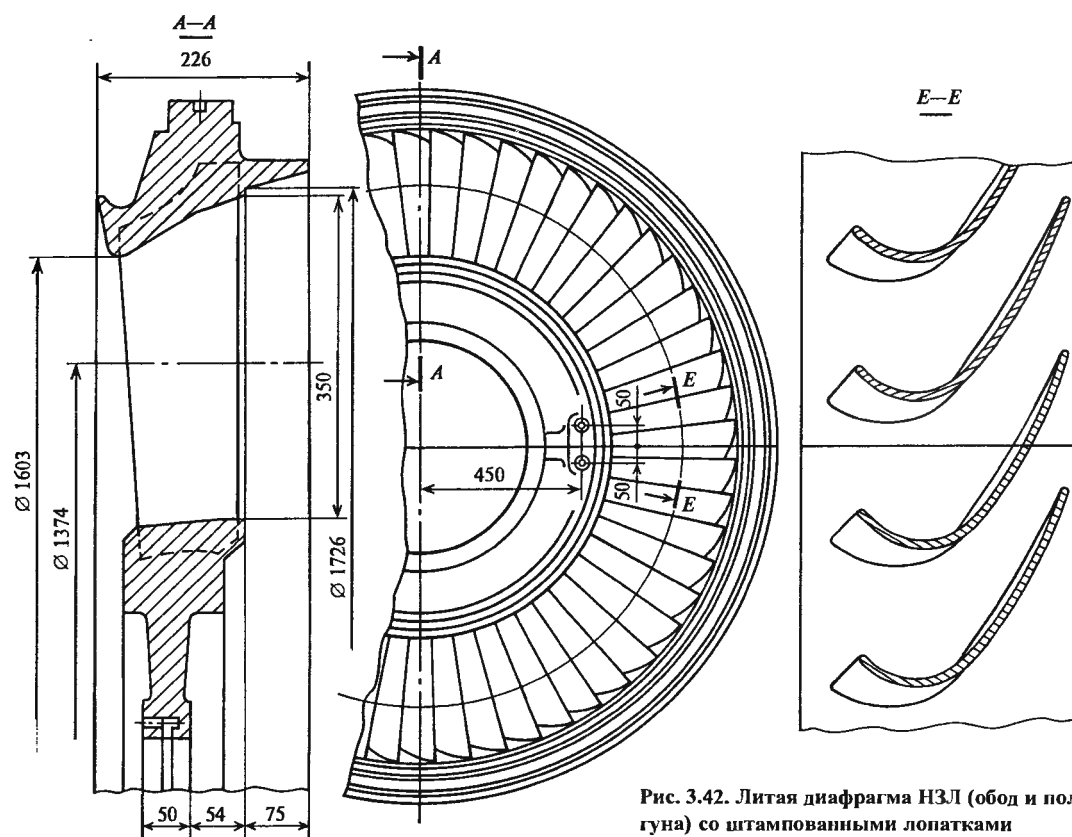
Литая диафрагма НЗЛ (обод и полотно отлиты из чугуна) со штампованными лопатками
